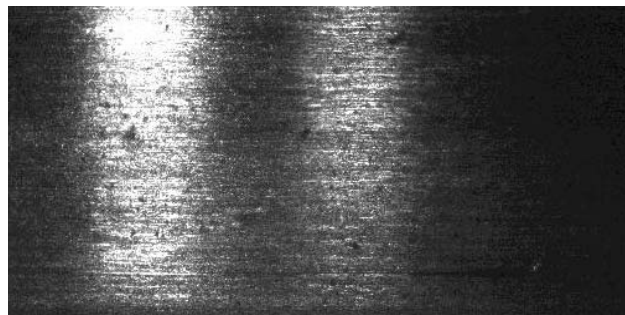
Шероховатость поверхности при обработке пластиной VCGT 160408-AZ
